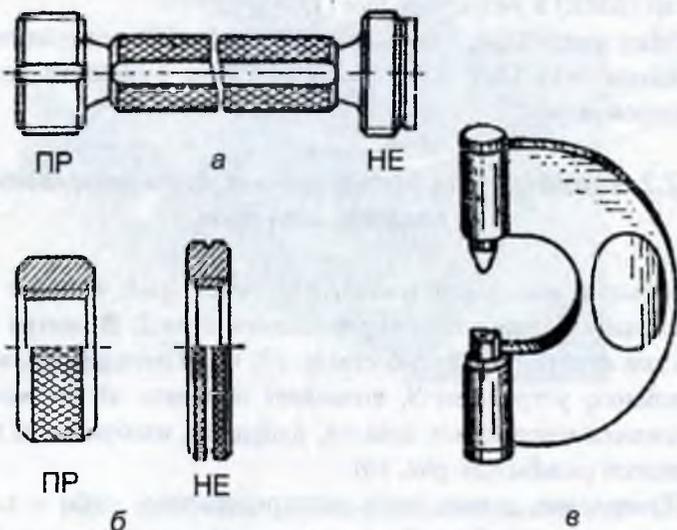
Предельные резьбовые калибры: а – двусторонняя пробка; б – резьбовые кольца; в – резьбовая скоба с конической и призматической вставками
